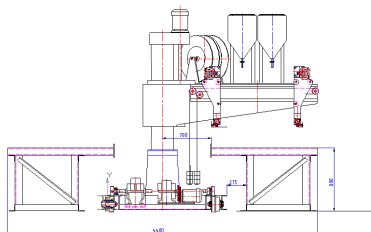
Зовнішній вигляд верстата для зварювання двутаврів
